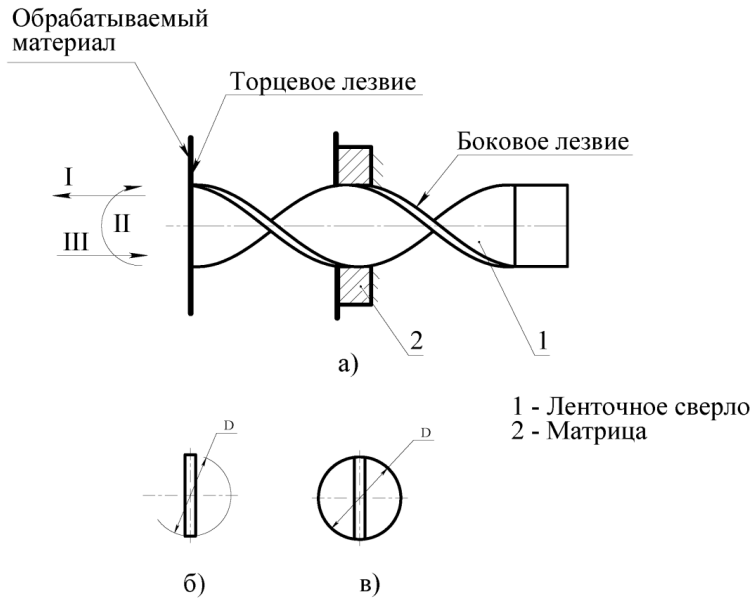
Схема обработки отверстия: а)-рабочее положение сверла и матрицы; б) и в)-формы вырезаемых отверстий
